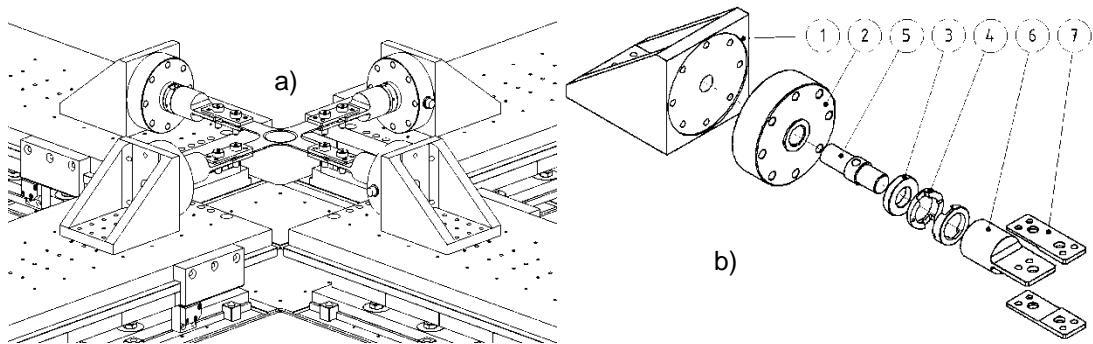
Detalhe da montagem do provete: a) Conjunto de fixação; b) Vista explodida do conjunto de fixação de um braço do provete e célula de carga.
